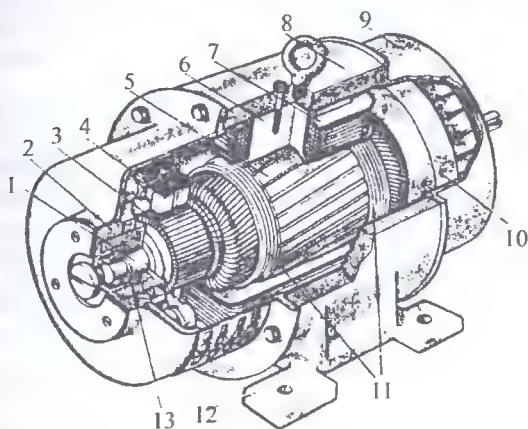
Устройство машины постоянного тока: 1 — вал; 2, 9 — подшипниковые щиты; 3 — коллектор; 4 — контактно-щеточный механизм; 5 — сердечник ротора с обмоткой; 6 — сердечник главного полюса; 7 — полюсная катушка; 8 — корпус (станина); 10 — вентилятор; 11 — бандажи; 12 — лапы крепления; 13 — подшипник
